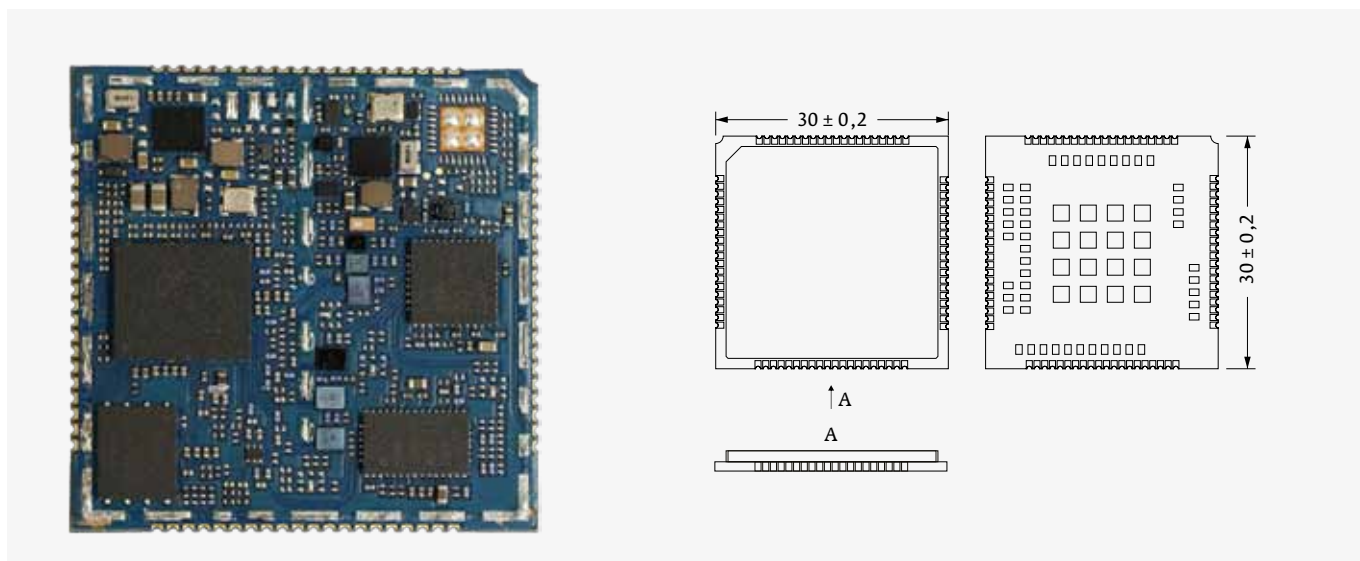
Внешний вид и размеры модуля ПР1603НБ
